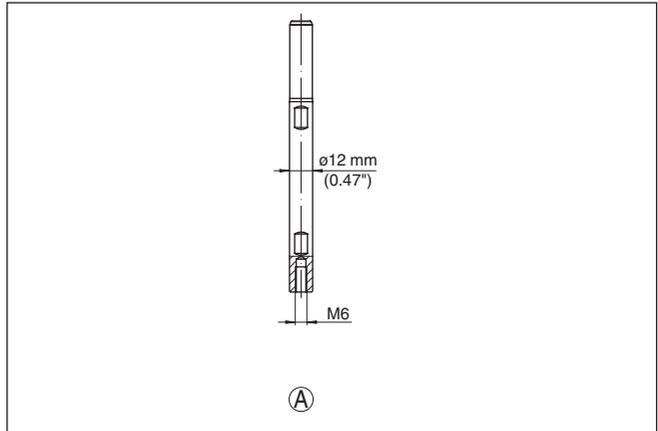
Stabkomponenten mit \varnothing 12 mm (0.47 in) - Basisstab
